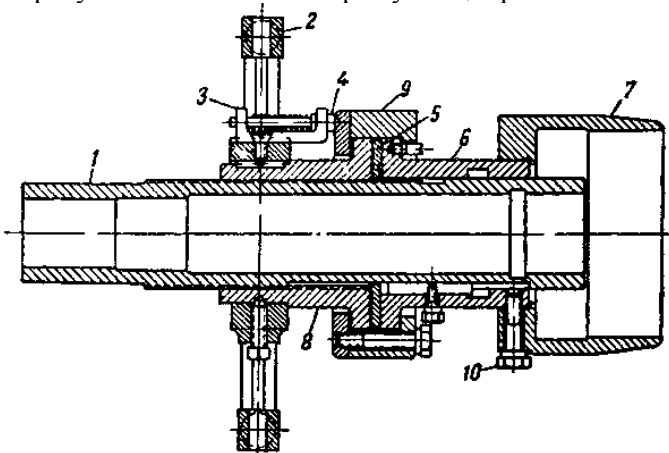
Конусний затиск для форпресів: 1 – втулка; 2 – штурвал; 3 – скоба; 4 – стопор; 5 – замикаюче кільце; 6 – втулка; 7 – регулюючий конус; 8 – гайка; 9 – обойма; 10 – болти
